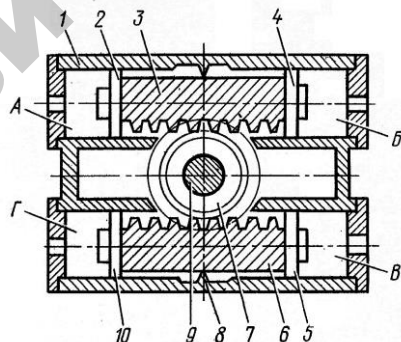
Поршневой поворотный гидродвигатель:
